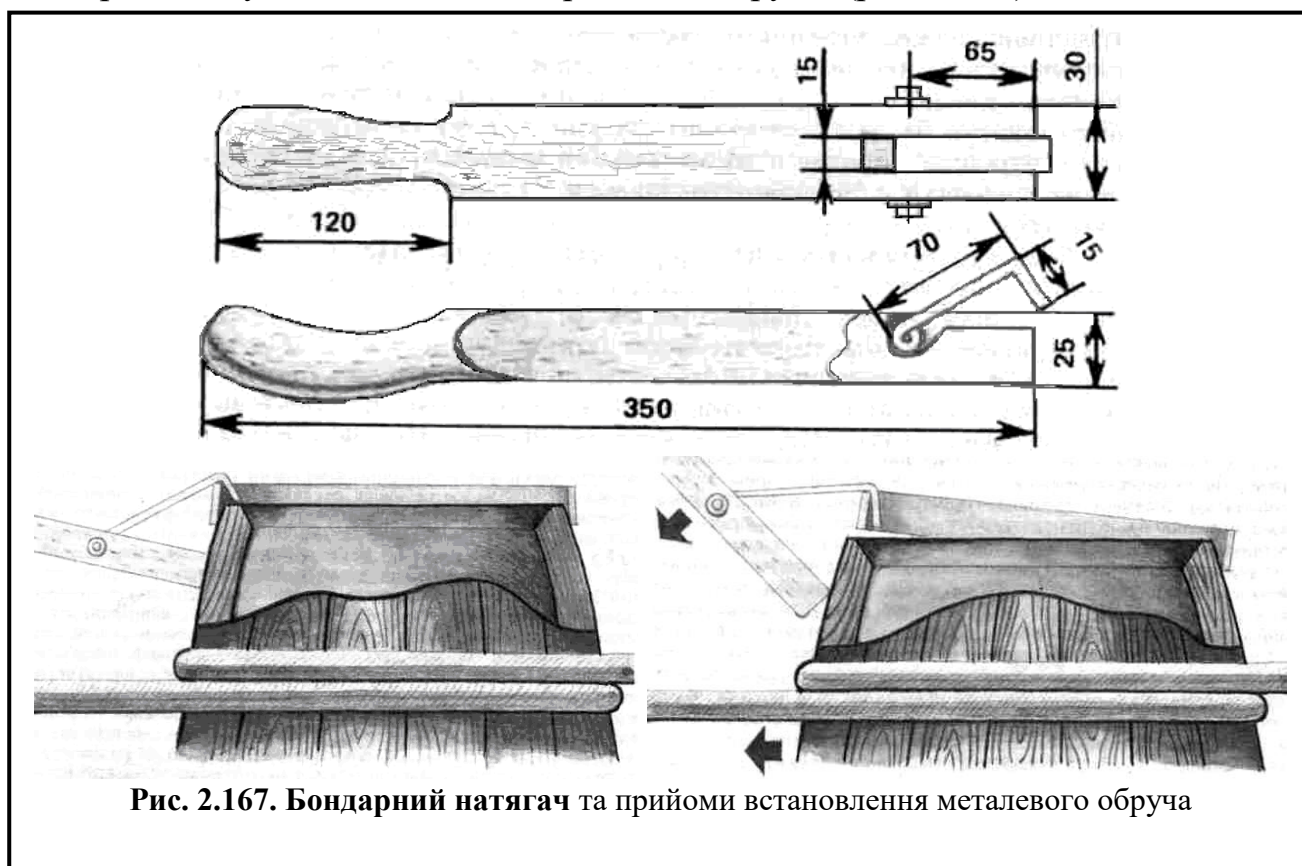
Бондарний натягач та прийоми встановлення металевого обруча
